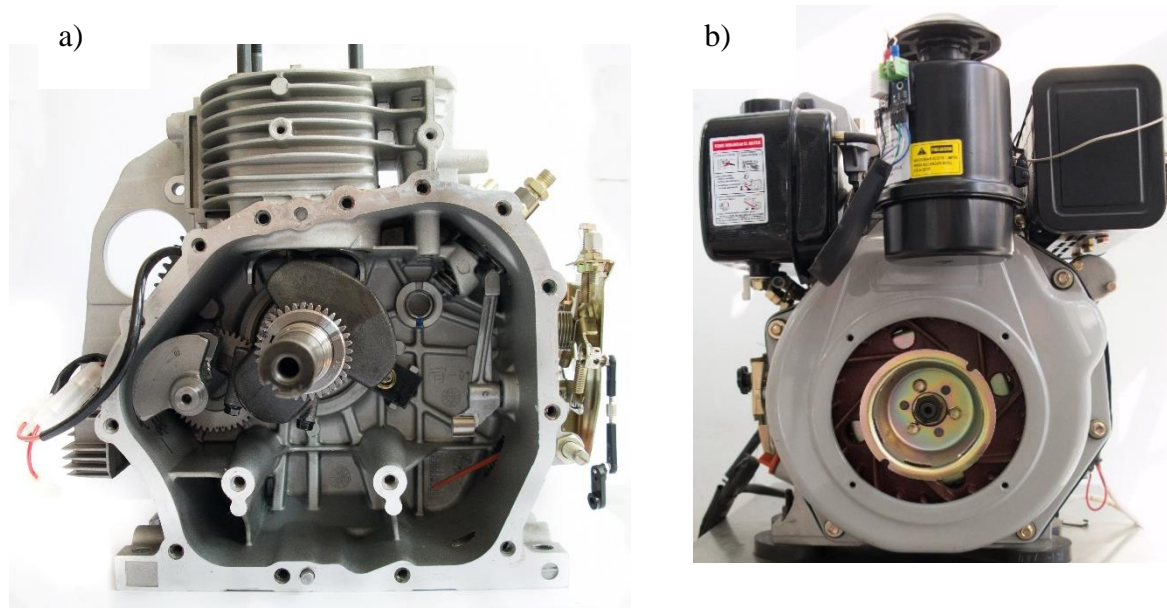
Sistema de combustión motor desarrollado en el presente trabajo, a) vista frontal sin tapa, b) vista posterior: I) tanque de combustible II) filtro de aire y III) escape del motor
